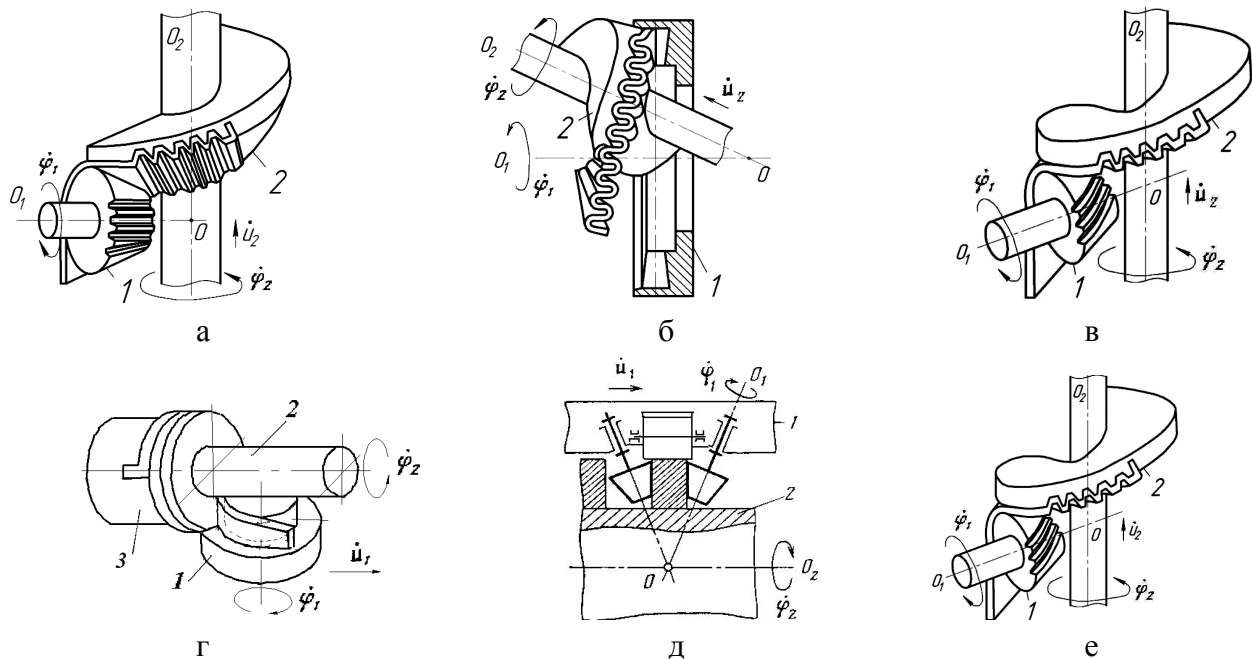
Схеми формоутворення ГЗ за допомогою інструментів з робочими поверхнями у вигляді гелікоїда та гіперболоїда обертання:
